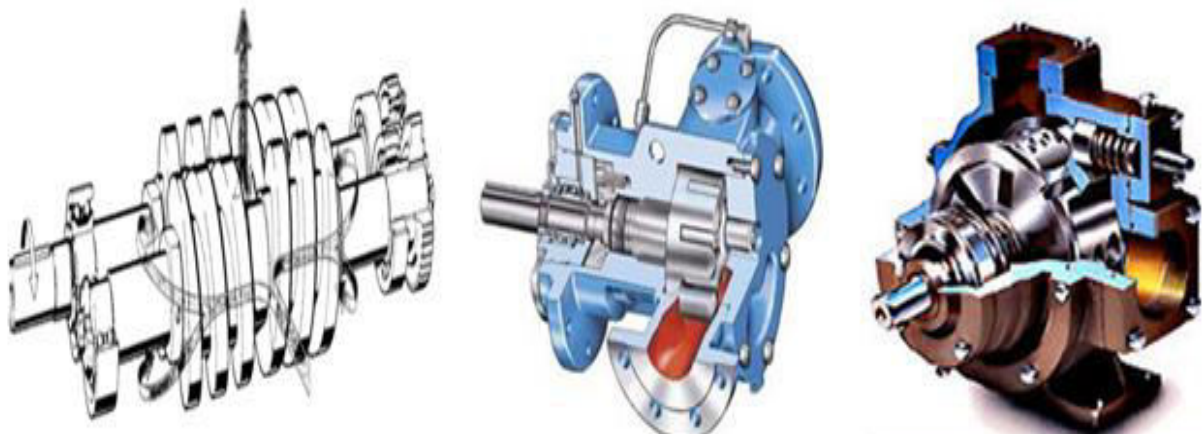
Ejemplos de bombas rotativas de tornillo, engranajes y álabes (de izquierda a derecha)
